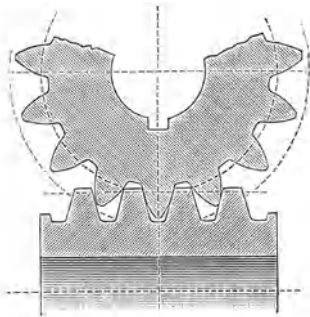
Schneckenrad mit korrigierter Zahnform.
